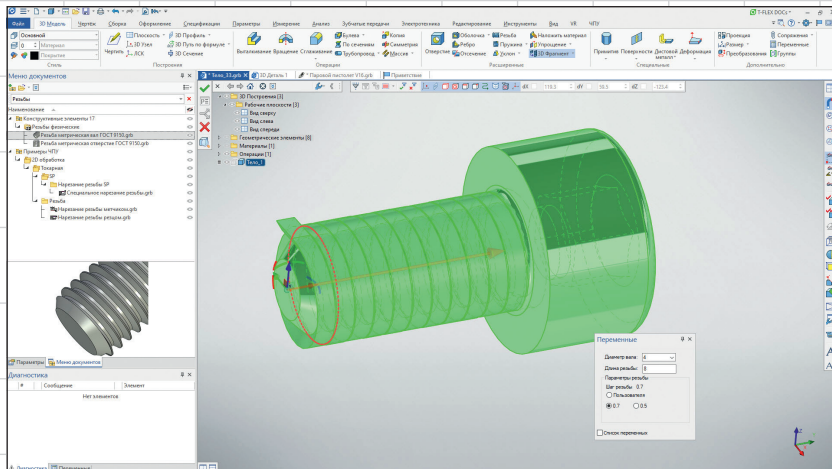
Процесс построения физической резьбы T-FLEX CAD 17
